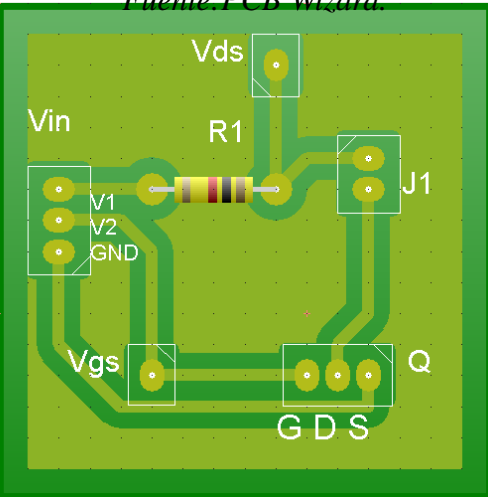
Diseño de PCB *Fuente:PCB Wizard.
